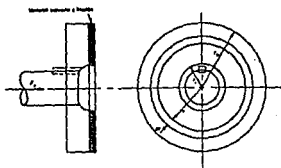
Vista en sección transversal de un conjunto típico de embrague de un solo plato
